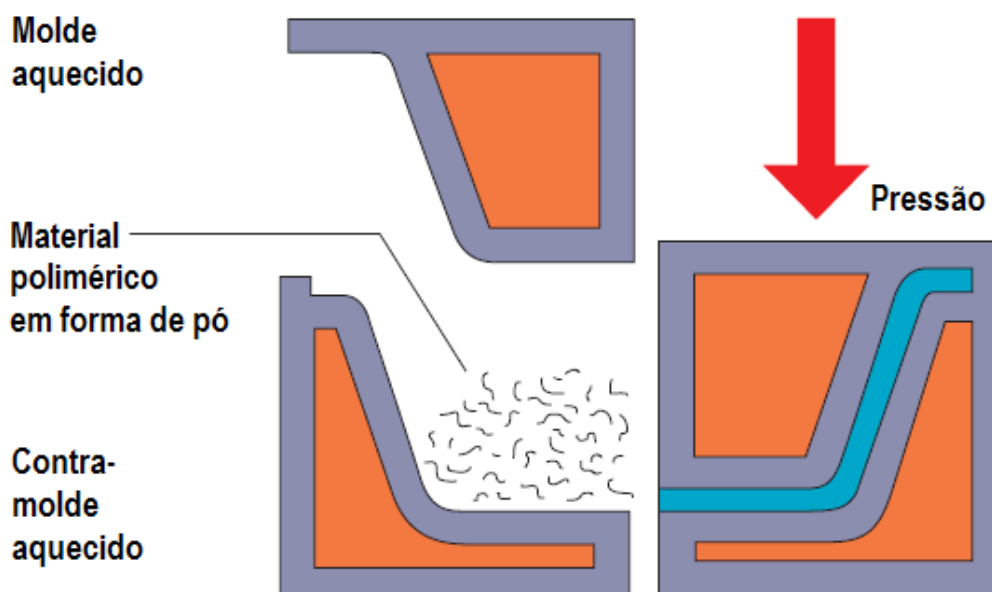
Representação esquemática da moldagem por compressão [8].
